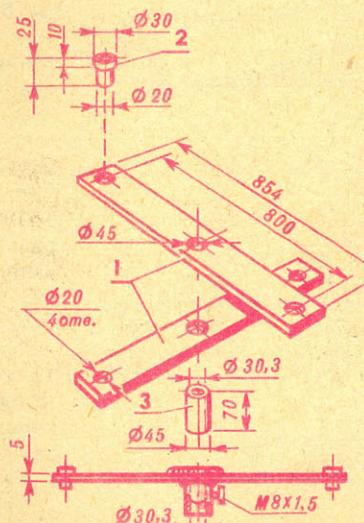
Верхняя крестовина крепления лопаток ротора в сборе:
